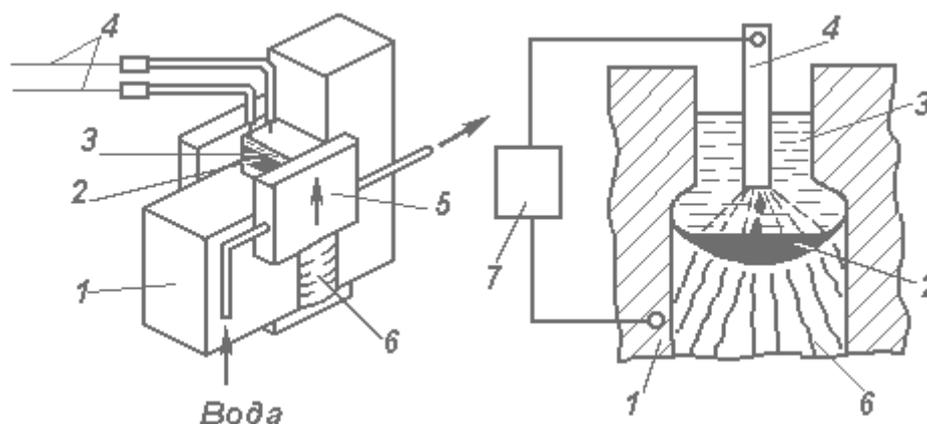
Схема процесса электрошлаковой сварки
